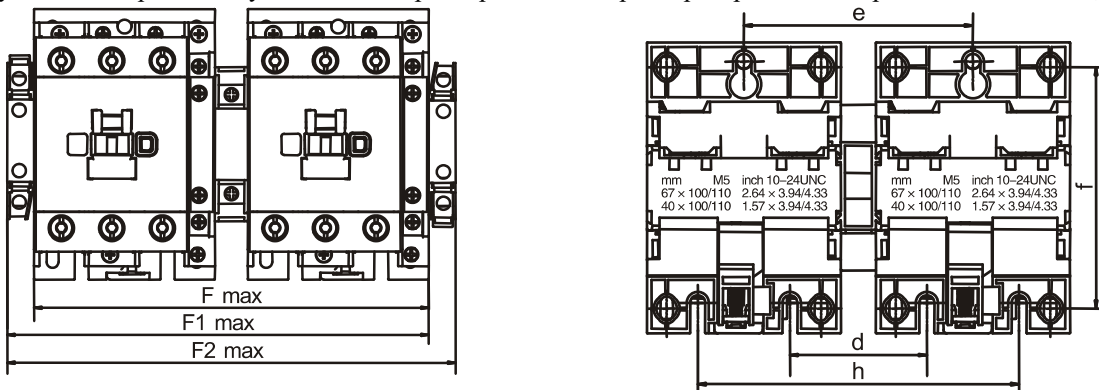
Габаритные и установочные размеры контакторов с реверсивной сборкой на токи 40-95А, мм.
